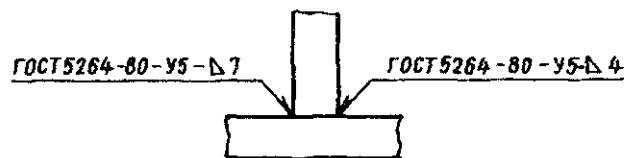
Обозначение двусторонних угловых сварных швов
